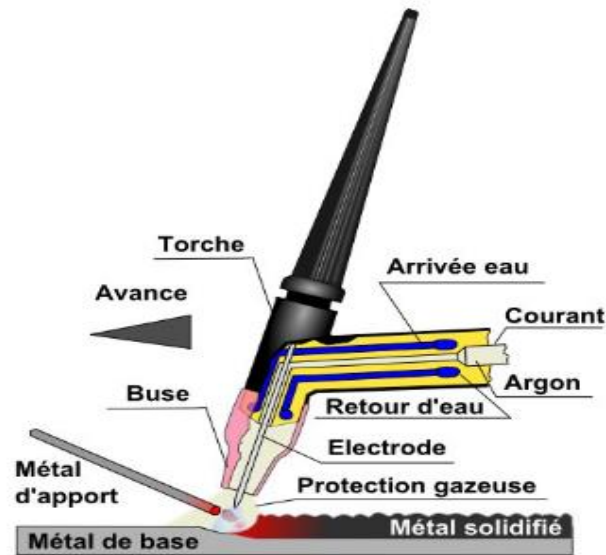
Principe du procédé de soudage TIG [23]
